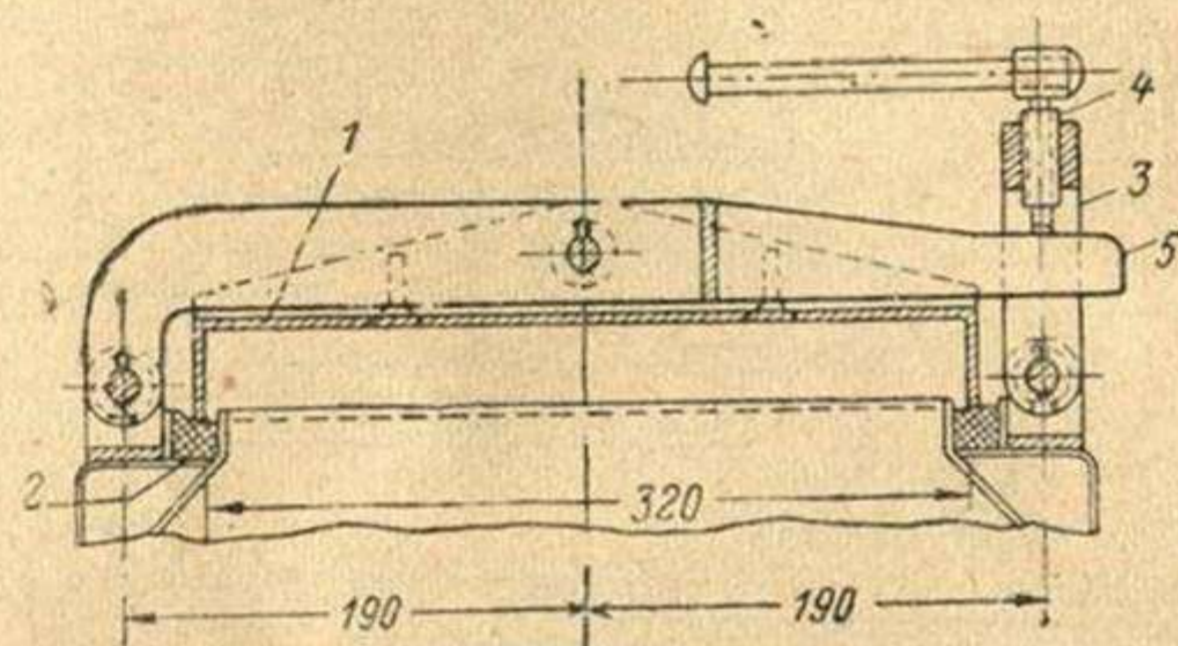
Загрузочный люк газогенераторной установки Ш-Ц:
